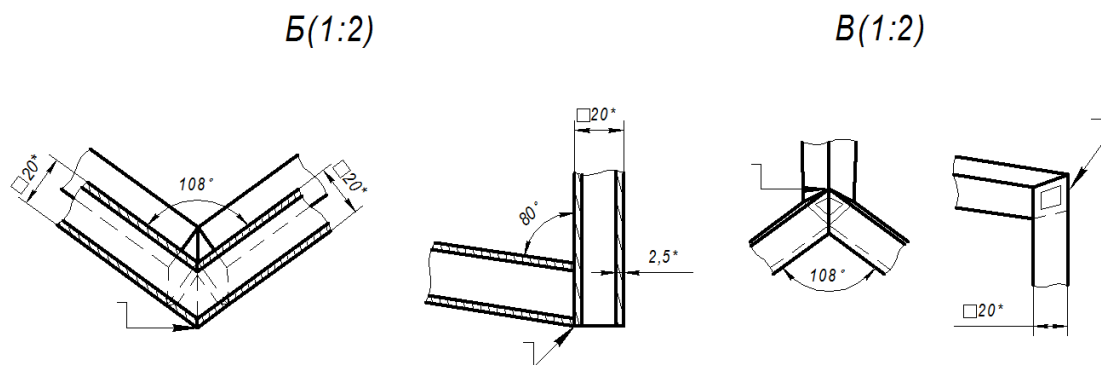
Зварні з'єднання деталей каркасу підстілля
